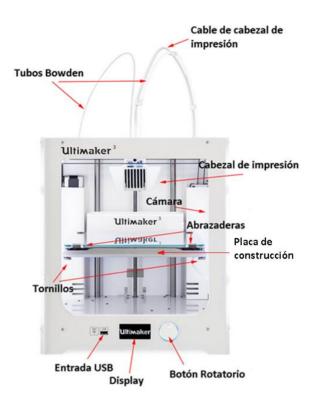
Partes principales de la impresora 3D vistas desde la cara frontal.
